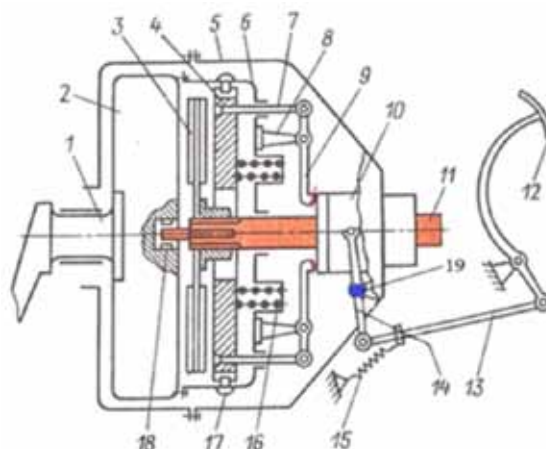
Сцепление трактора: 1 — коленчатый вал; 2 — маховик; 3 — ведомый диск с фрикционными накладками; 4 — нажимной диск; 5 — картер сцепления; 6 — кожух сцепления; 7 — оттяжной палец; 8 — опора оттяжного рычага; 9 — оттяжной рычаг; 10 — муфта выключения сцепления; 11 — ведущий вал коробки передач; 12 — педаль; 13 — тяга; 14 — вилка выключения; 15 — оттяжная пружина; 16 — нажимная пружина; 17 — направляющий палец; 18 — ролик подшипник; 19 — датчик углового перемещения
